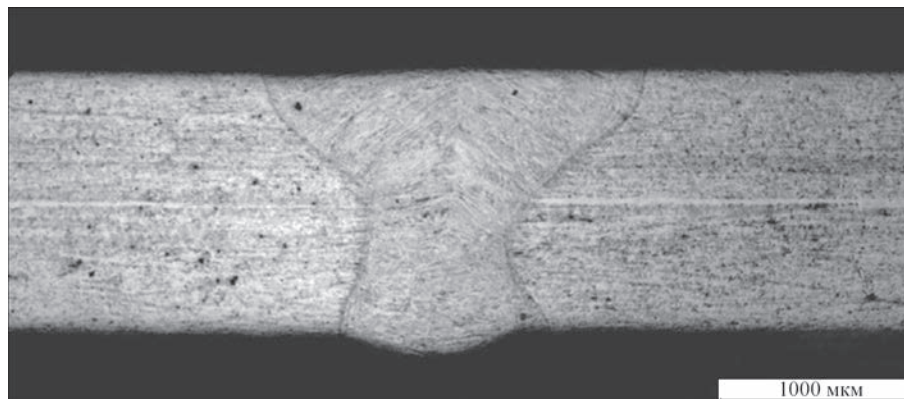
Макроструктура стыкового соединения стали SUS304 ( $\delta = 1,5$  мм), полученного лазерно-микроплазменной сваркой без применения присадочной проволоки
